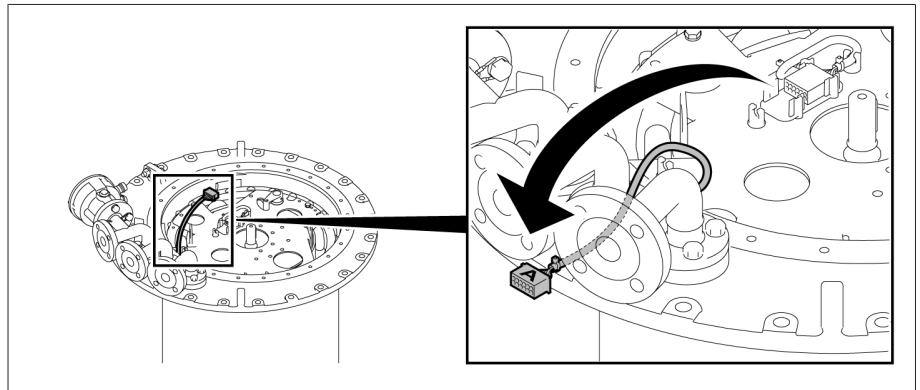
Giro hacia fuera de la pieza A de la conexión de enchufe
